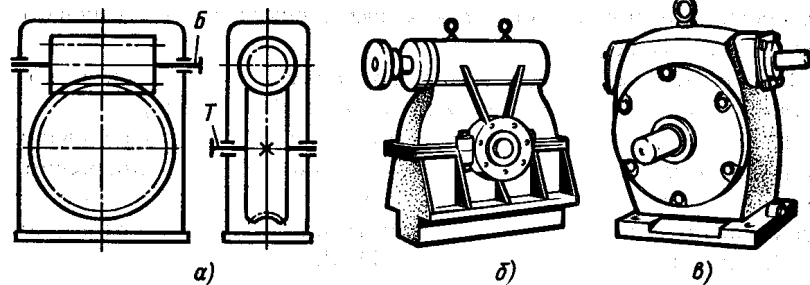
Червячный редуктор с верхним расположением червяка:
